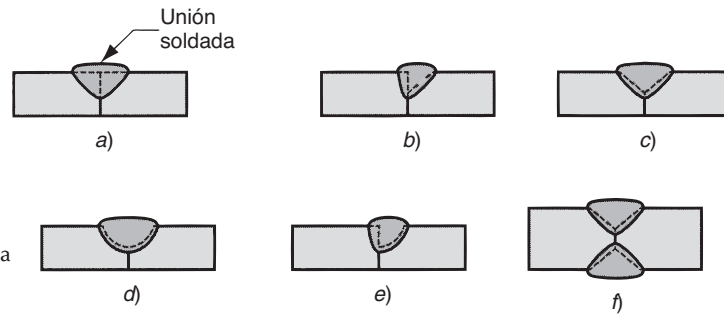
Algunas soldaduras con surco típicas: a) soldadura con surco cuadrado, un lado; b) soldadura con surco en bisel único; c) soldadura con surco en V único; d) soldadura con surco en U único; e) soldadura con surco en J único; f) soldadura con surco en V doble para secciones más gruesas. Las líneas punteadas muestran los bordes originales de las piezas.
